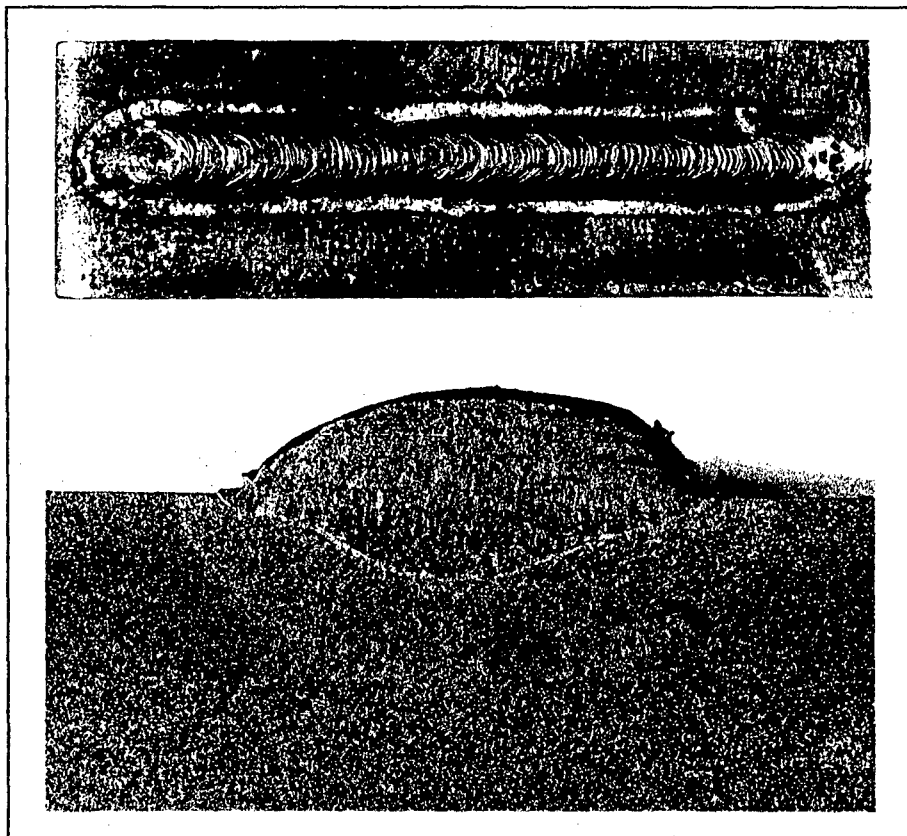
Aspecto do cordão de solda para o eletrodo A em CA.
